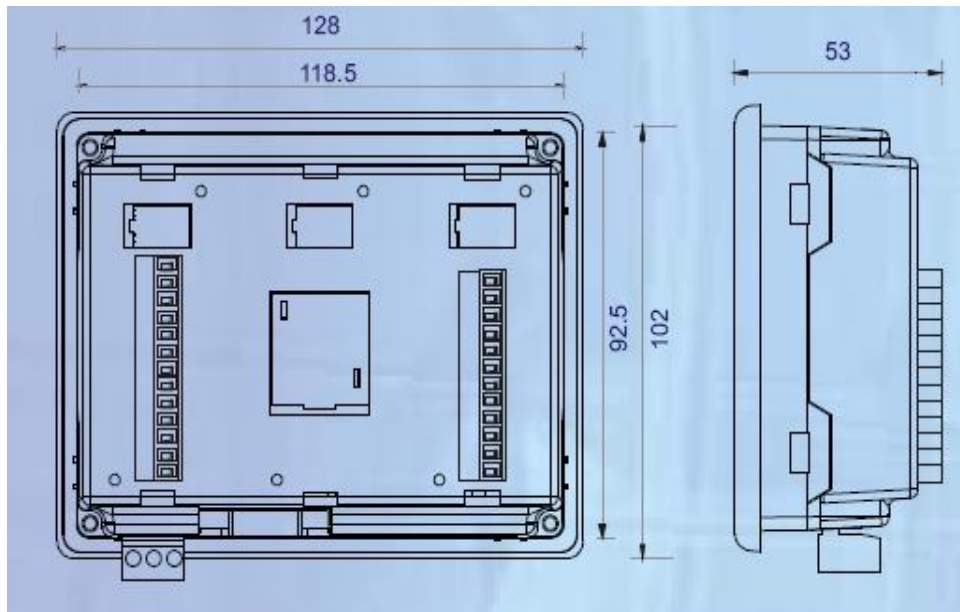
Dimensiones de (panel mounting and panel cut-out) - PLC FP4030MR-L1208R.
